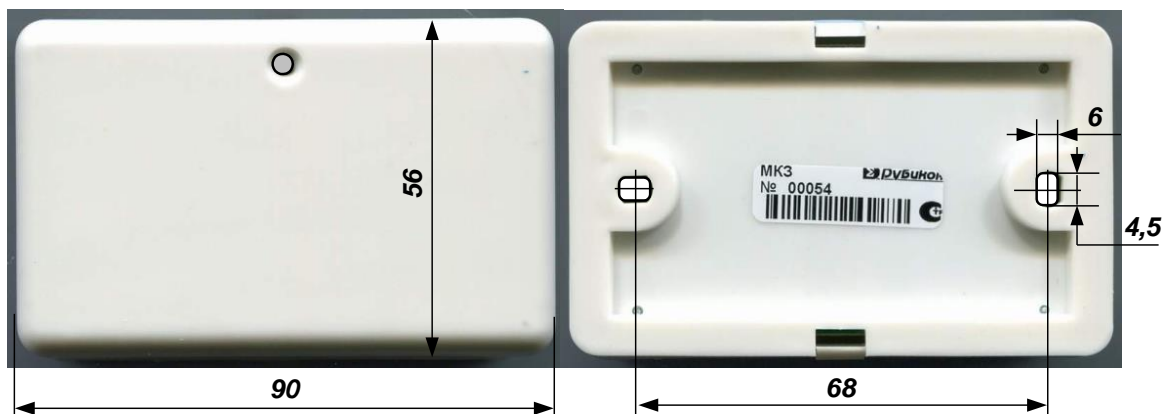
Габаритные и присоединительные размеры корпуса МКЗ
